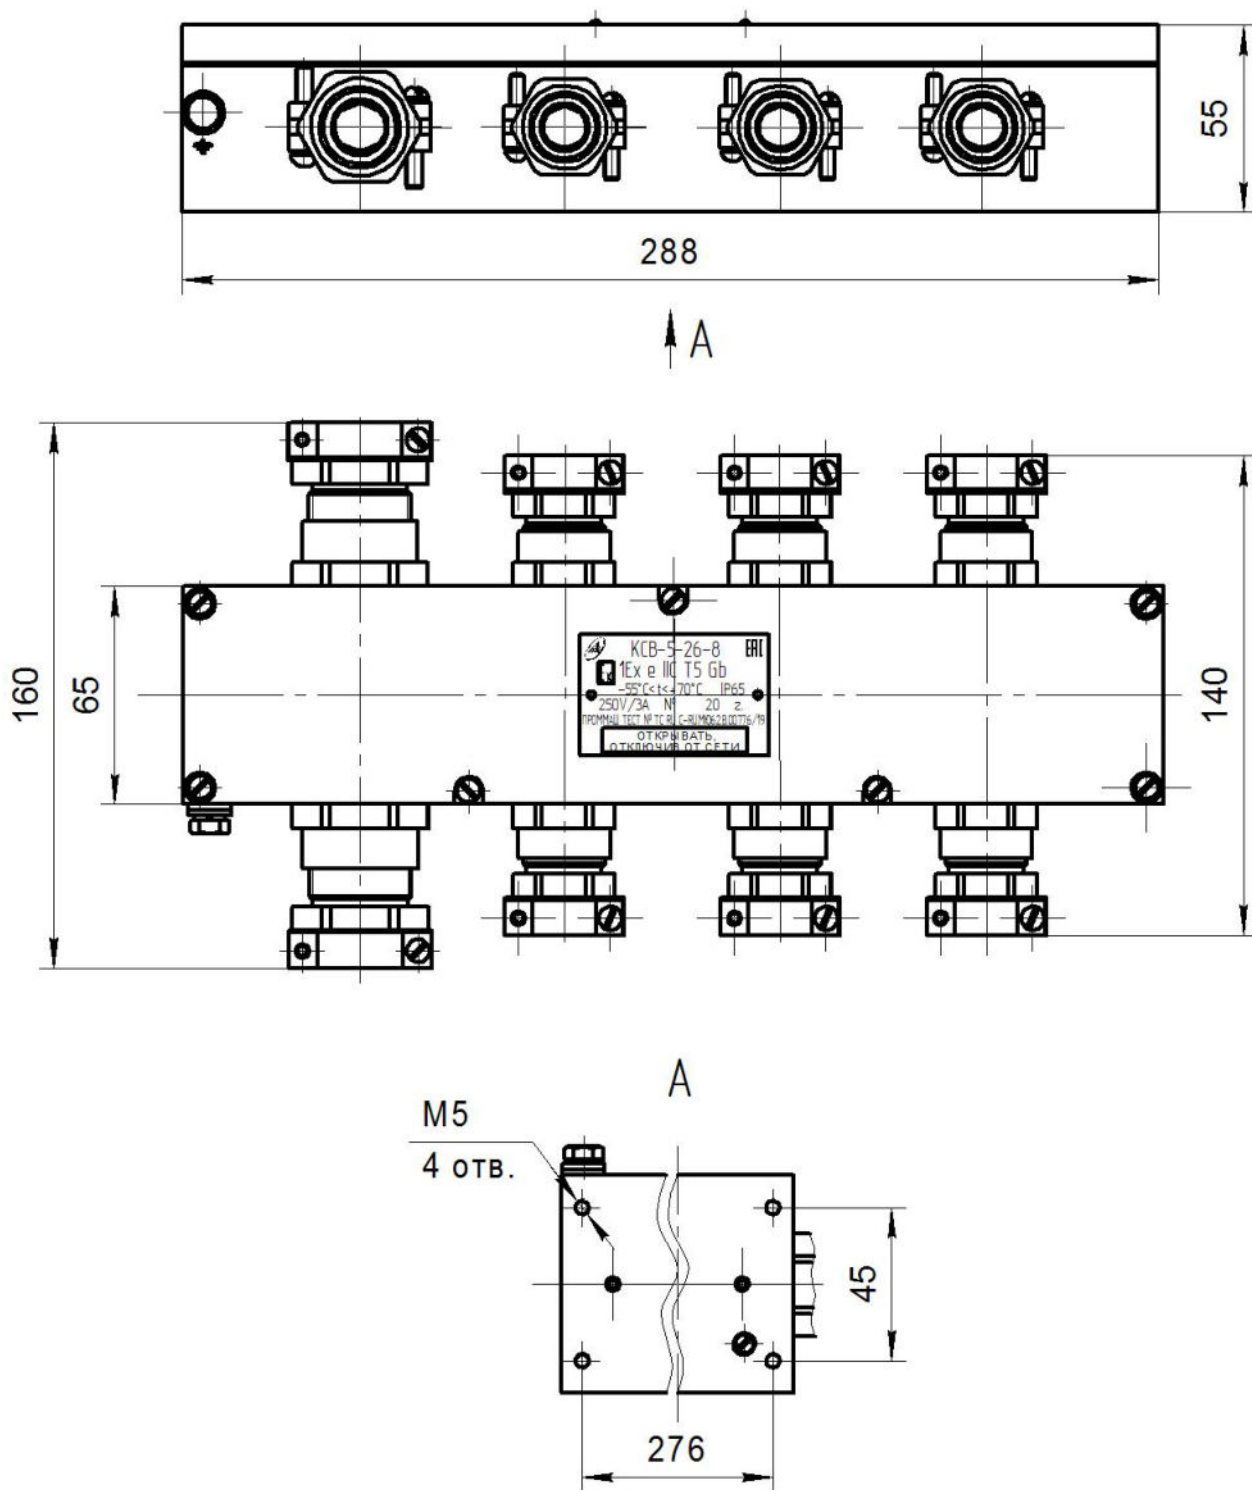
Внешний вид и присоединительные размеры коробки KCB-5-26-8
